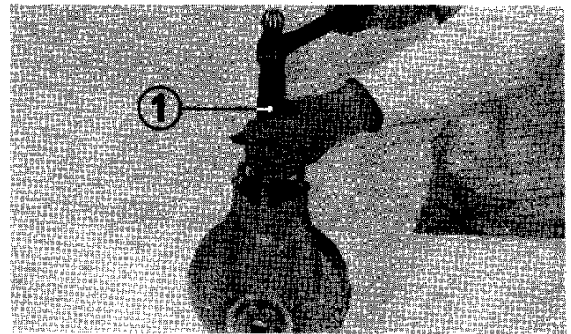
(1) Wellenringdichtung-Treibwerkzeug
